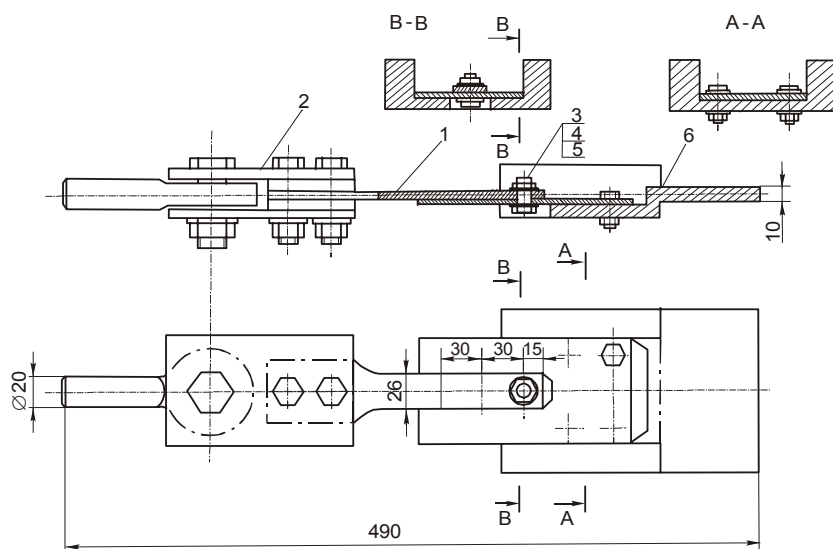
Приспособление для исследования усталостной долговечности односрезовых болтовых соединений из сплава ВТ6:
